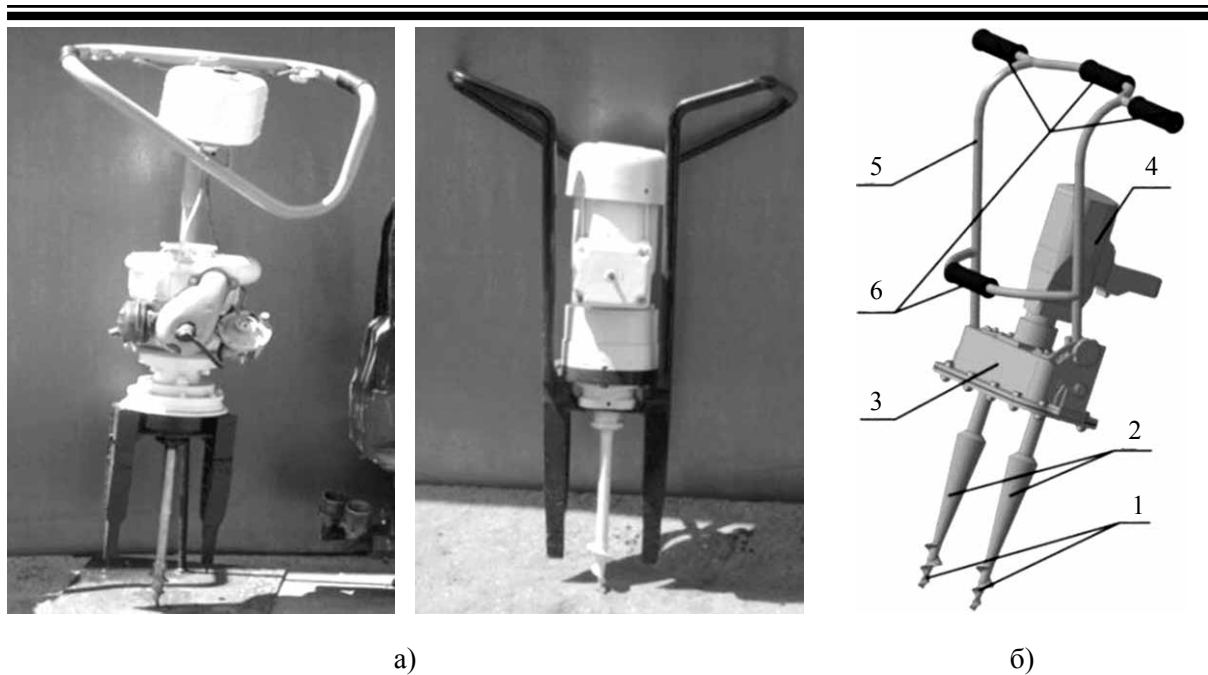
Ручной мерзлоторыхлительный инструмент: а) старая конструкция; б) новая конструкция инструмента с двумя винтовыми наконечниками: 1 – винтовые наконечники; 2 – рыхлящие штанги; 3 – корпус; 4 – привод; 5 – рама; 6 – рукояти
